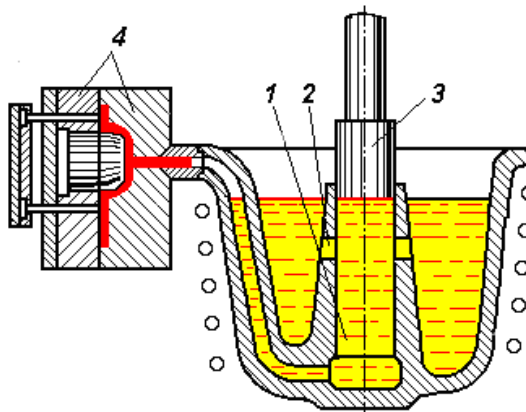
Машина для литья под давлением с горячей вертикальной камерой прессования
